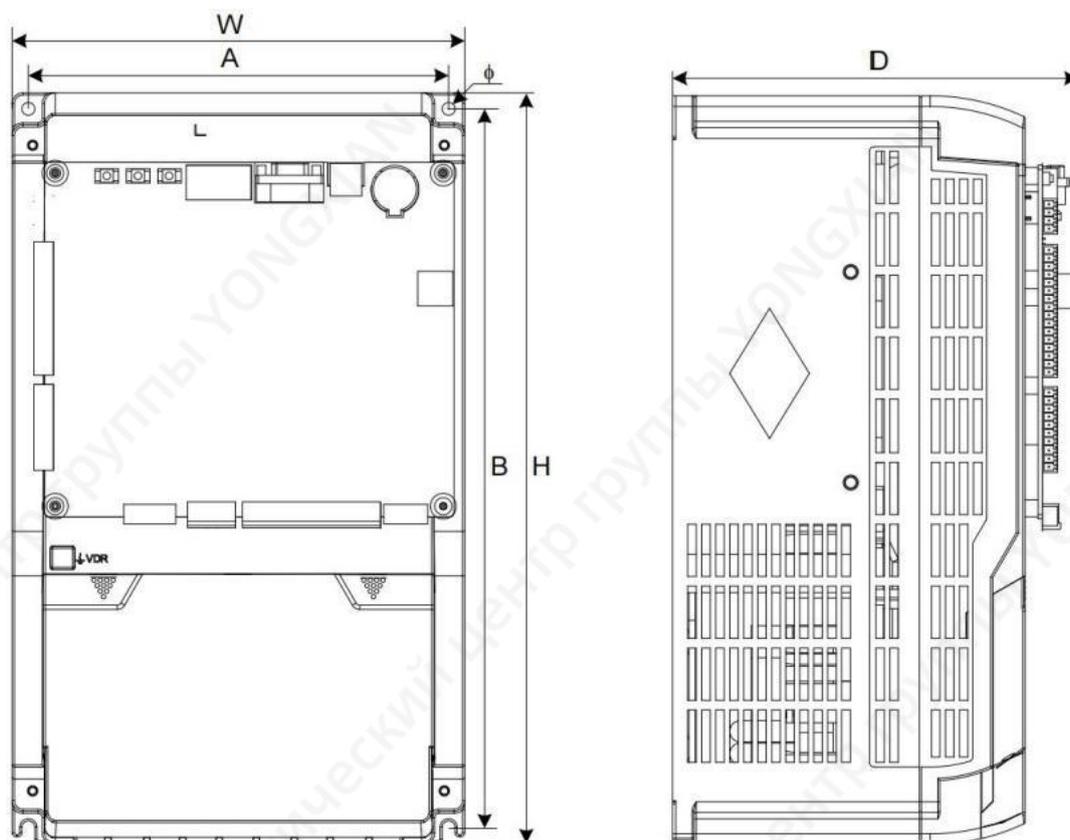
[Модель F]Обзор и установочные размеры пластиковой конструкции
